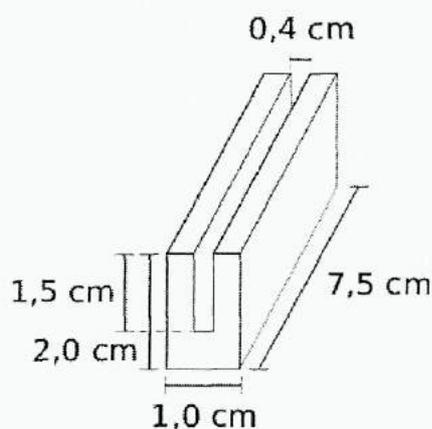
Desenho técnico do suporte do anteparo.
